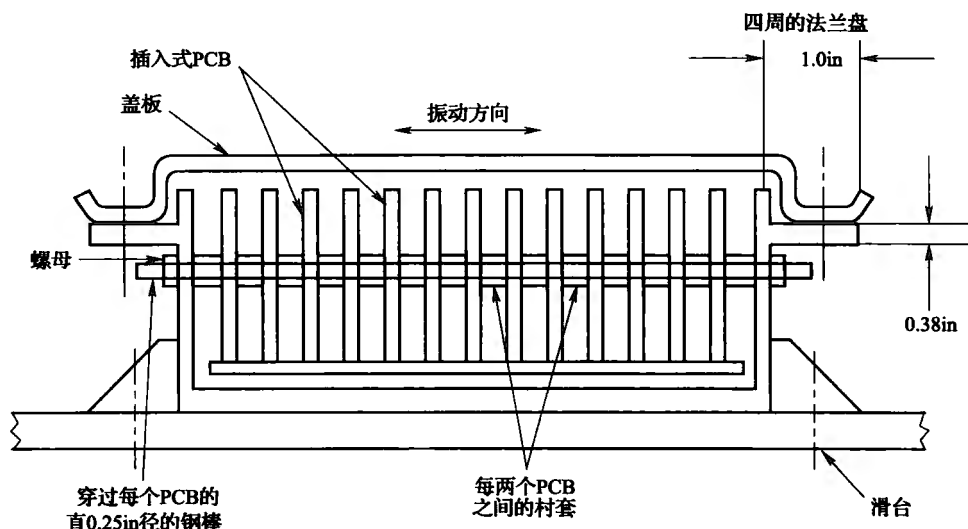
用于改善支撑以提高 PCB 固有频率的穿过每个插入式 PCB 中心的长钢棒，它未曾工作，高的动载荷破坏了底座
